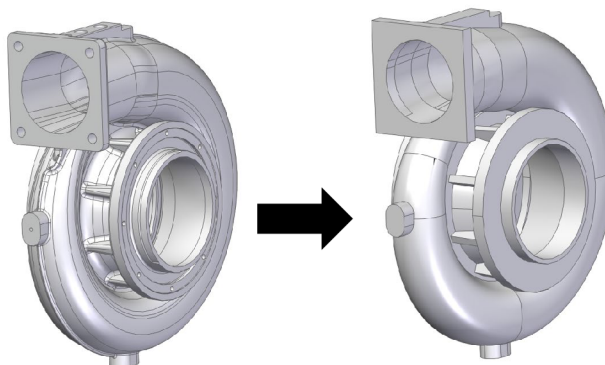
Úprava geometrie pro vložení do Ansys Mechanical
